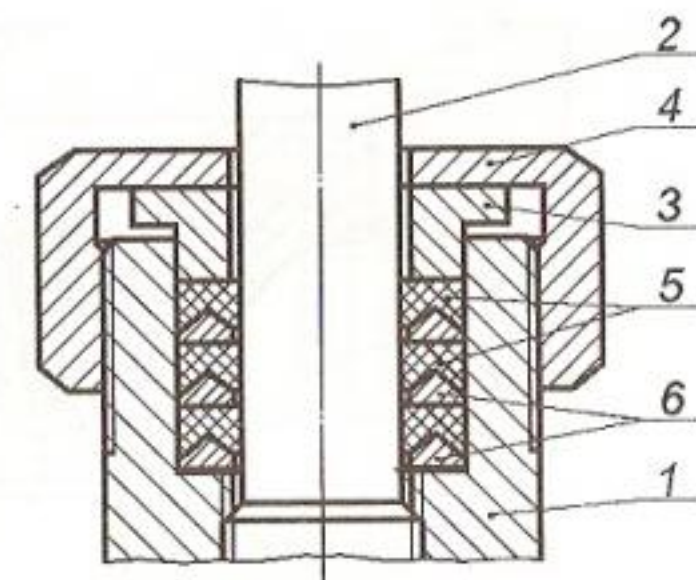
Уплотнение шпинделя с помощью уплотнительных колец из фторопласта (фрагмент вентиля: 1 – корпус; 2 – шпindel; 3 – втулка нажимная; 4 – гайка накидная; 5 – кольцо; 6 – шайба)
